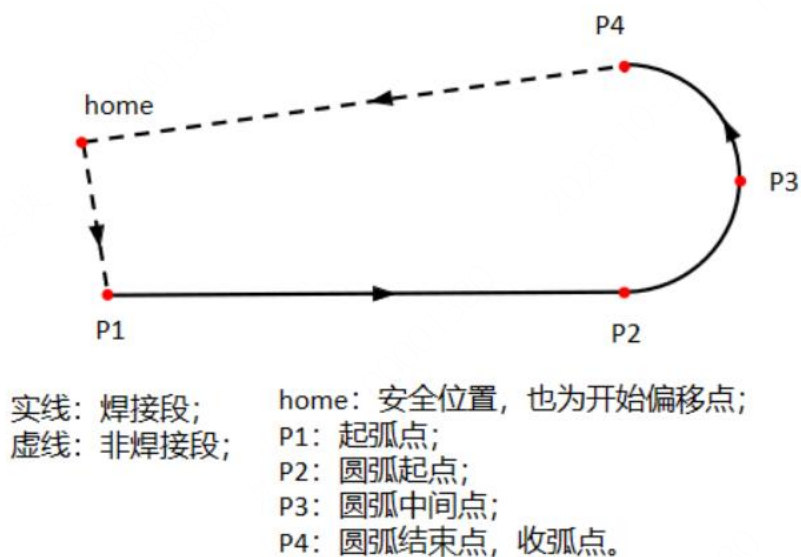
直线加圆弧单一方向多层多道焊示意图
